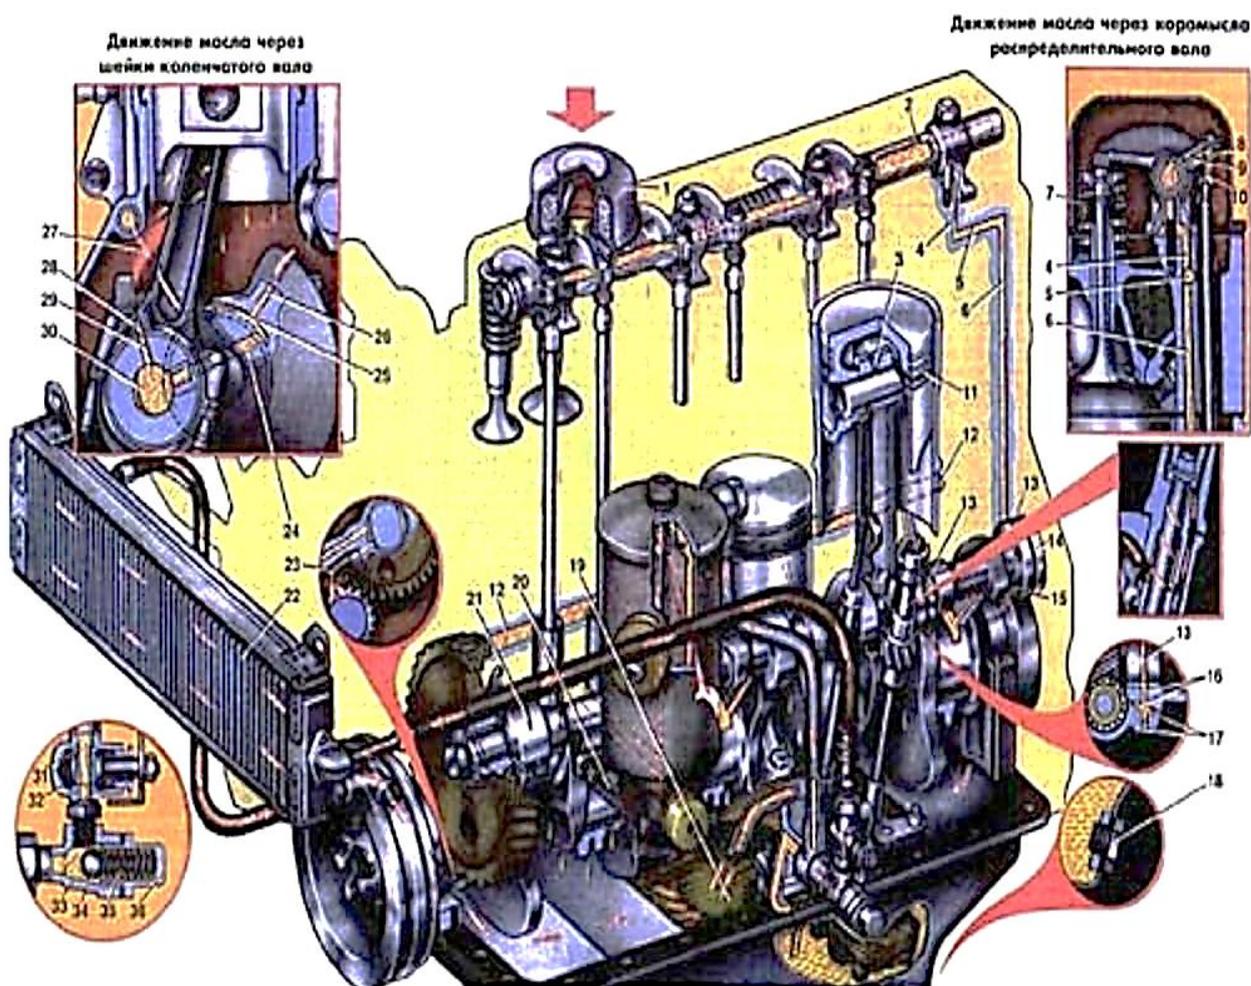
Смазочная система двигателя комбинированная: под давлением и разбрызгиванием
